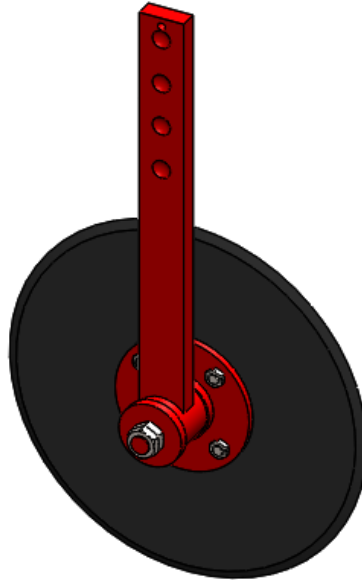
Vue en perspective du disque avec son support sur SolidWorks
